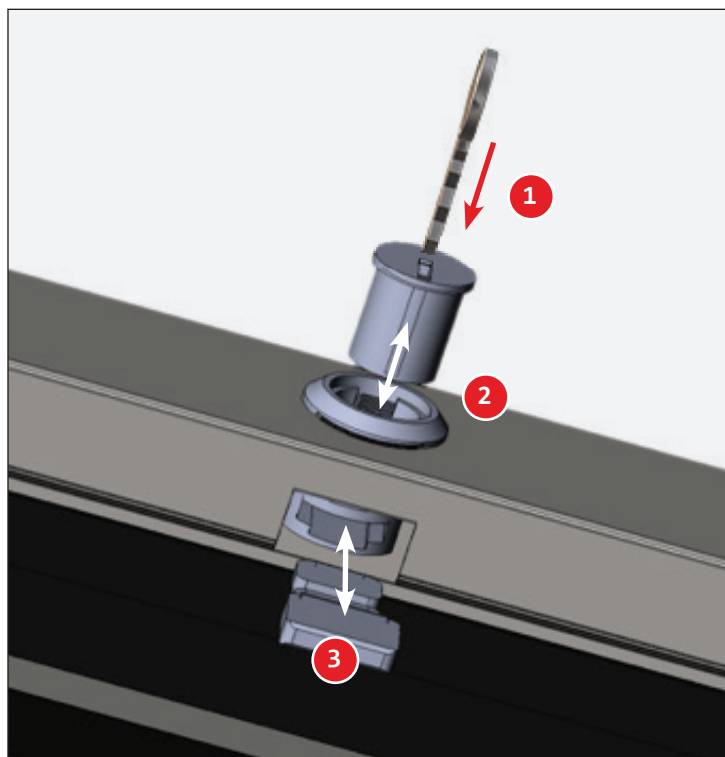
Vista dal basso della rimozione/installazione dei componenti.
